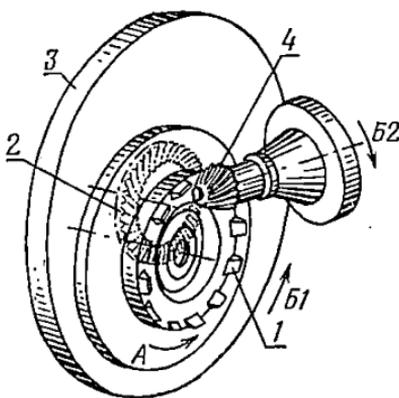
Нарезание конической шестерни с криволинейным зубом зуборезной головкой:
